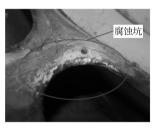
滑油散热风扇围框及操纵组合轴腐蚀 Fig. 5 Oil cooler and control shaft corrosion
